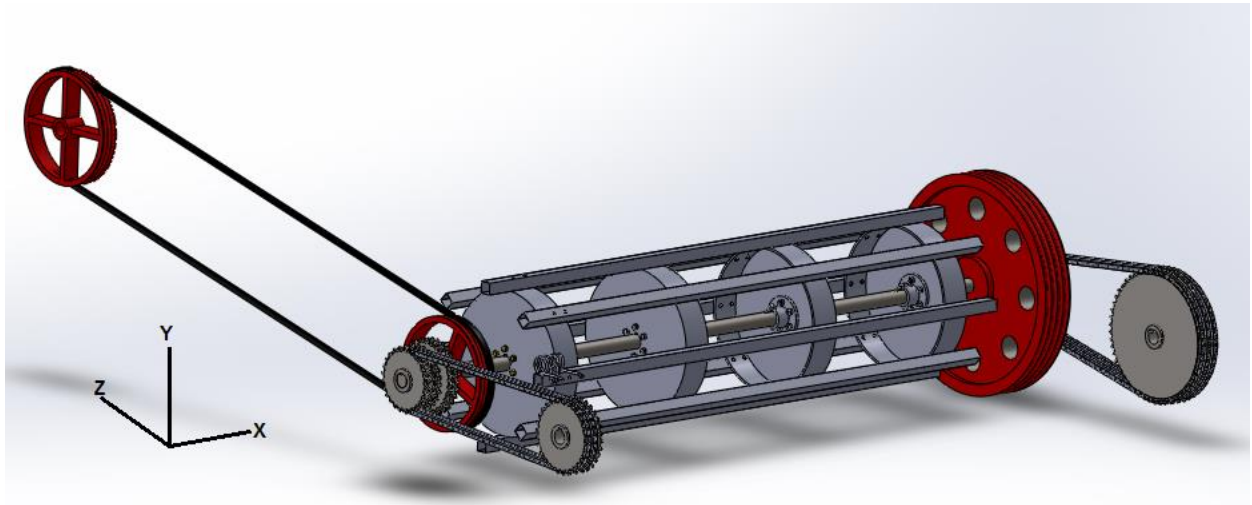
c) Segundo cilindro de trilla a dimensionar
